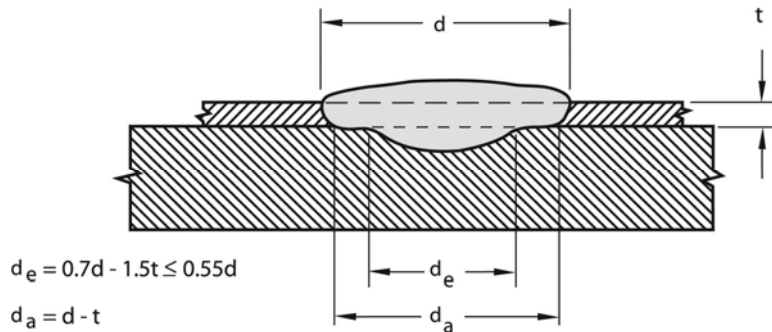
Soldadura de tapón — Espesor sencillo de lámina
